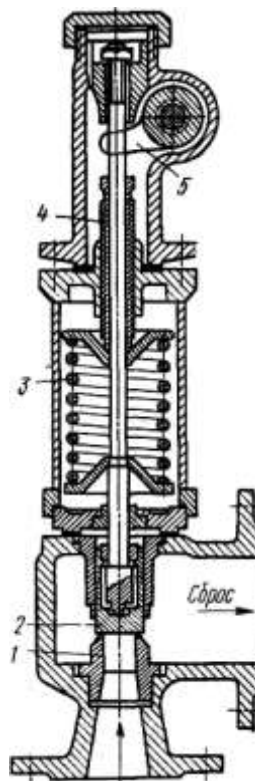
Запобіжний скидний клапан ЗСК-4: 1 - сідло клапана; 2- золотник; 3- пружина; 4 - регулювальний гвинт; 5 – кулачок
